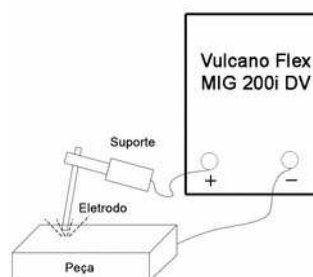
Conexão positiva para soldagem com eletrodo revestido
